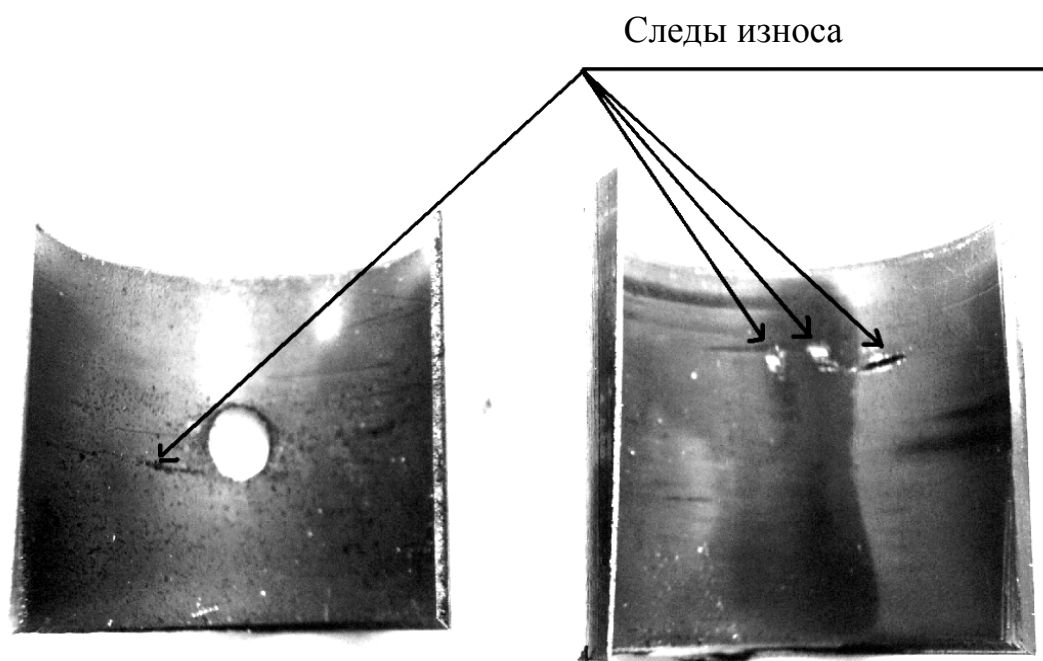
Характер износа втулки верхней головки шатуна двигателя ЗМЗ-53
